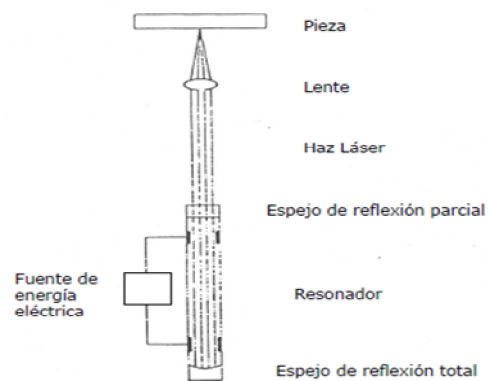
Instalación necesaria para la realización de una soldadura rayo láser [28].
